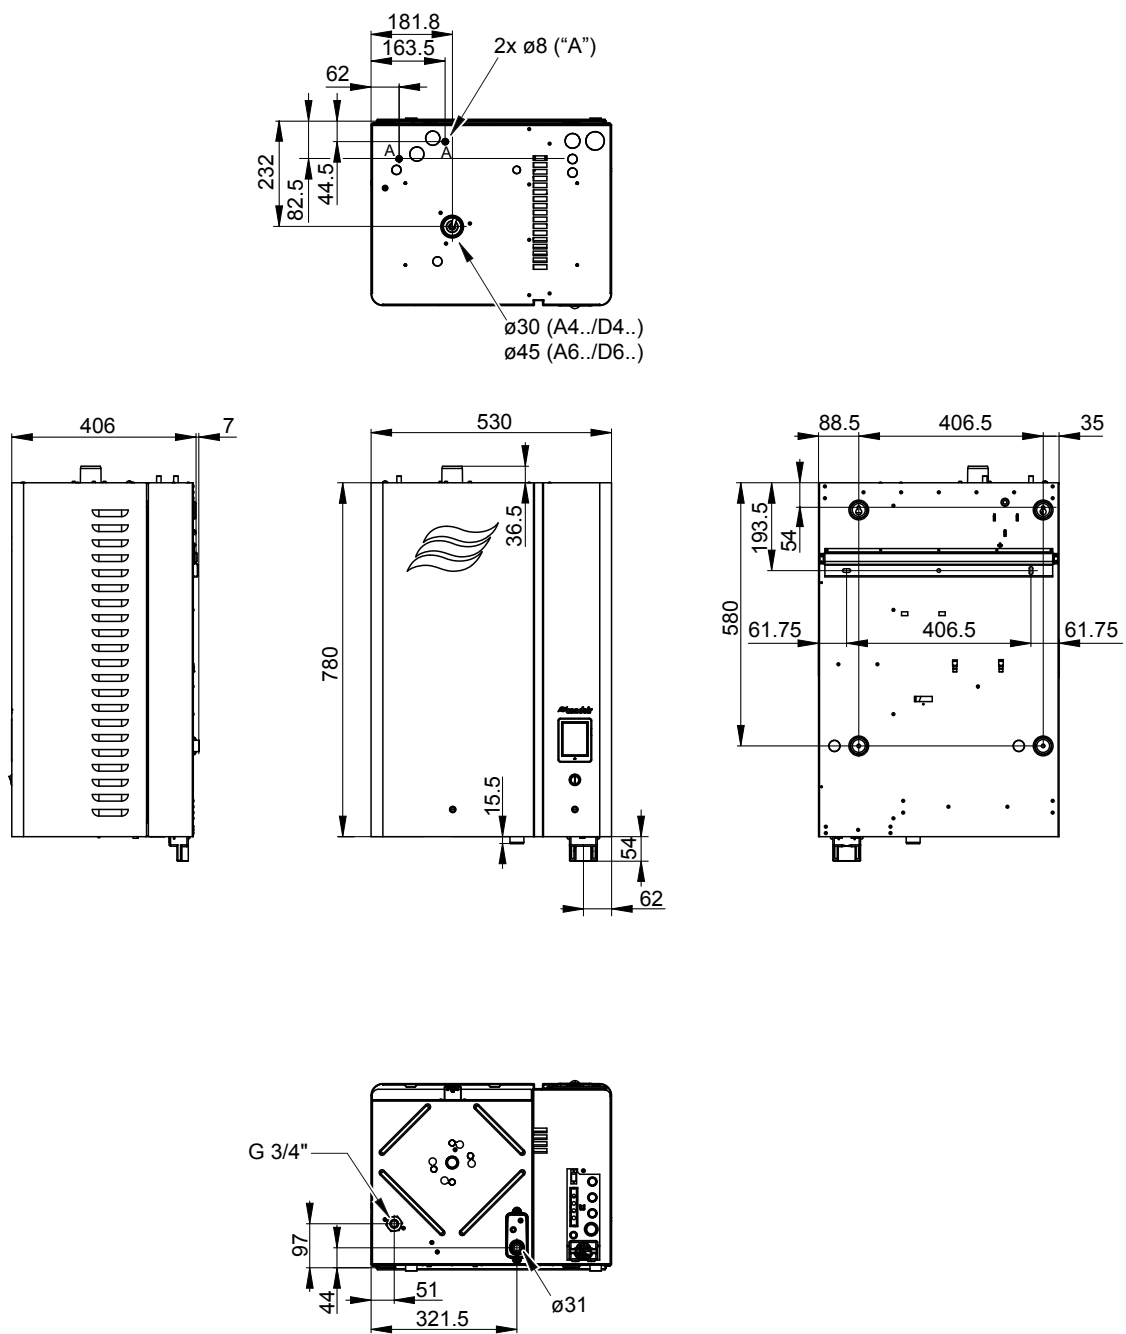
Figura de dimensiones Condair EL 20 - 45 y EL 35 - 180, tamaño de la carcasa "M" (dimensiones en mm)
